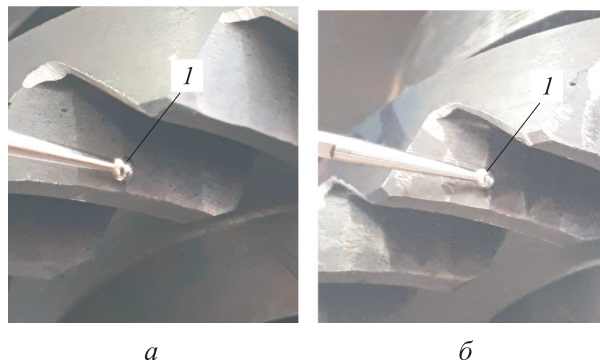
Измерение высоты огранки на боковой поверхности зуба спироидного колеса до (а) и после (б) обкатки (1 — ножка индикатора)
